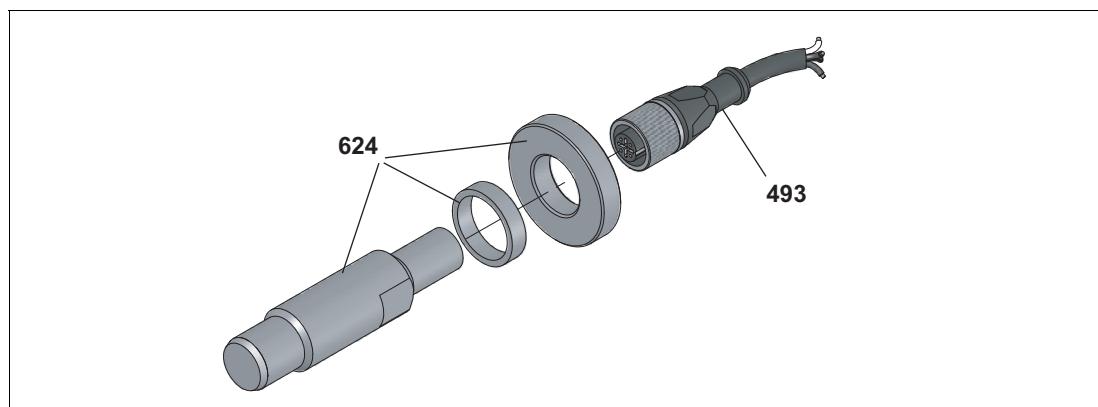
Explosionszeichnung BEG 53A/BEG 54A
